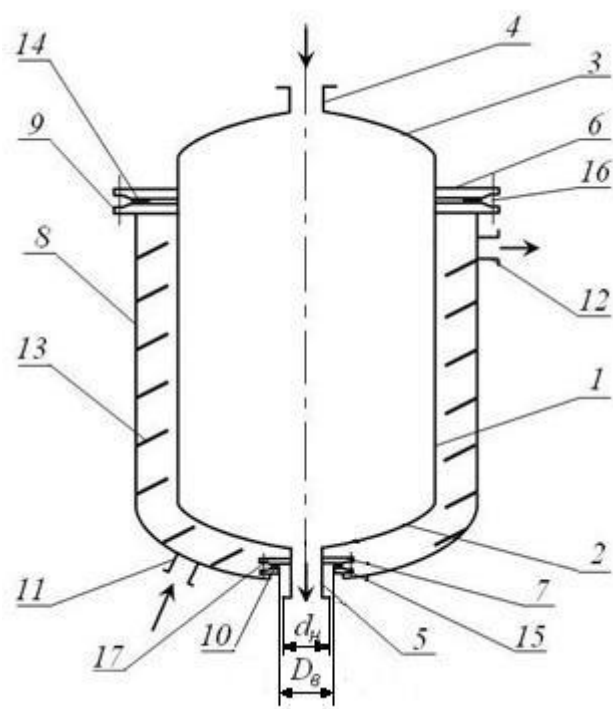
Общий вид реактора со съёмной U-образной рубашкой:
